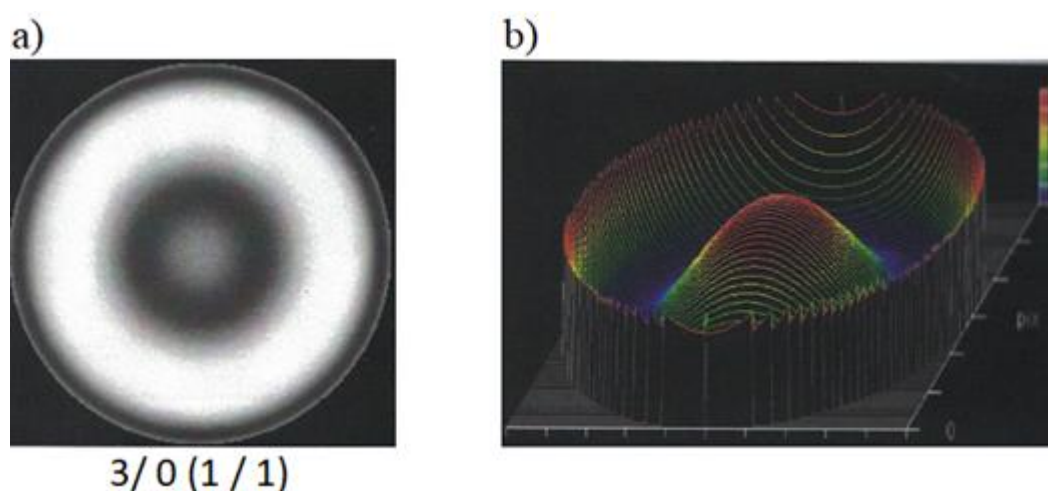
Interferenční obrazec se znázorněnou chybou výšky vrchlíku A. a) interferenční obrazec, b) izometrické zobrazení profilu
